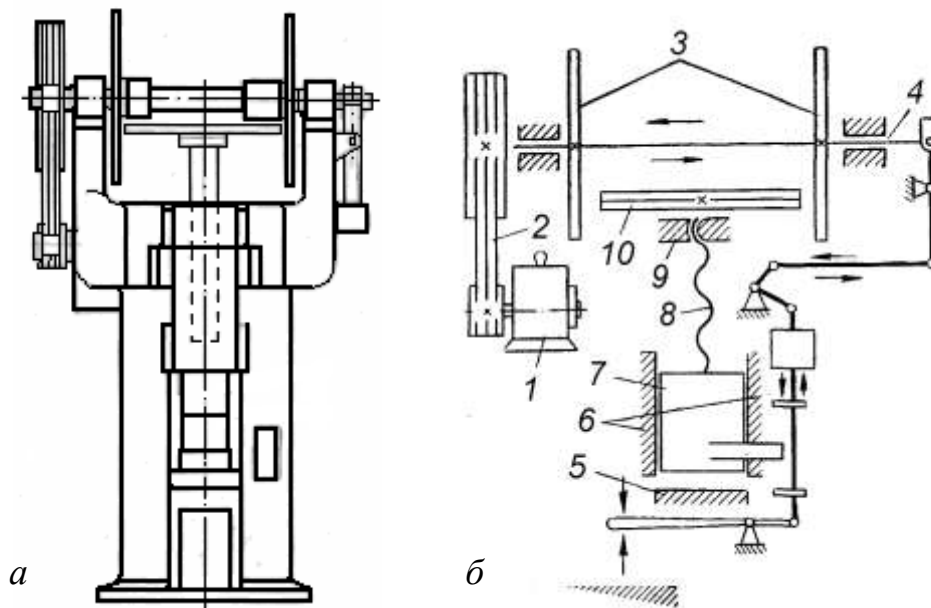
Гвинтовий прес (а – загальний вигляд; б – схема) [3]:
